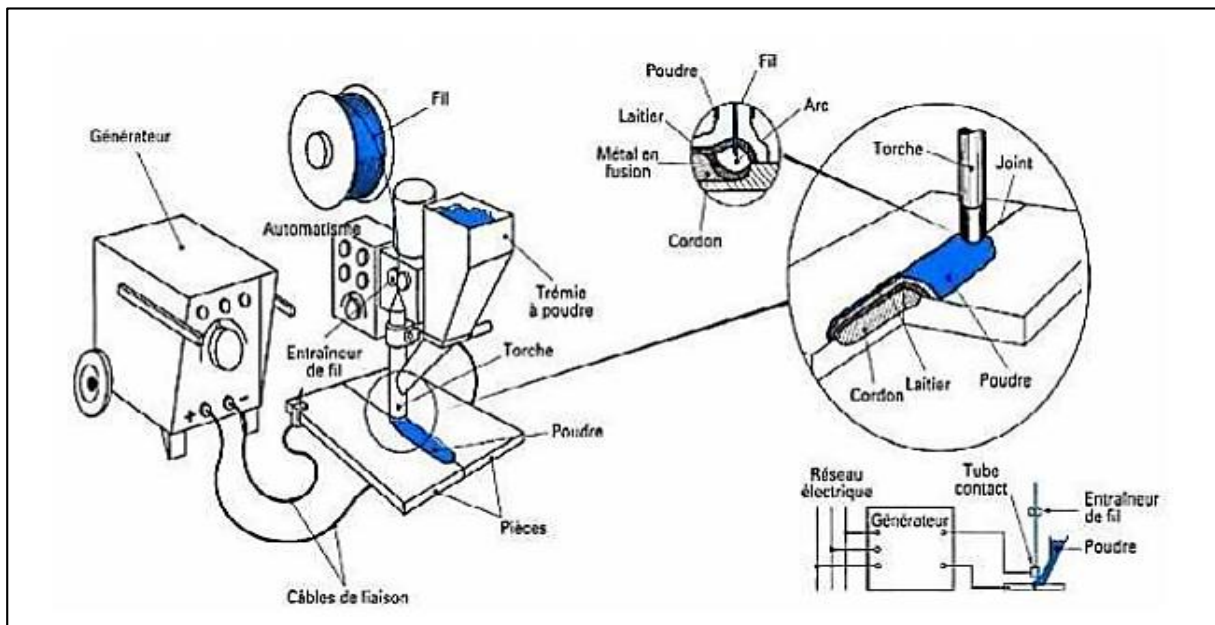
Principe de base du soudage à l'arc submergé SAW [3].
